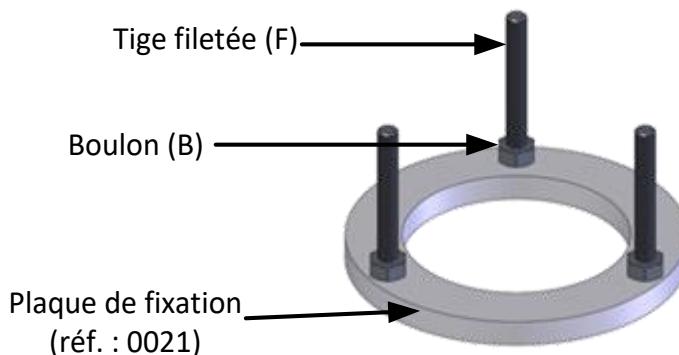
plaque de fixation prête à accueillir la bague de serrage
